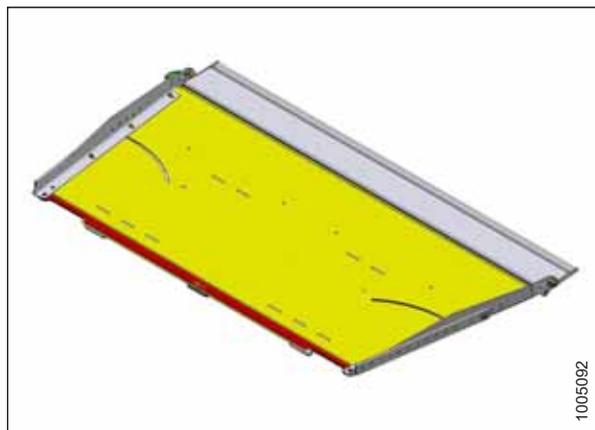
Формовочный щиток в сборе (MD № B4800)
